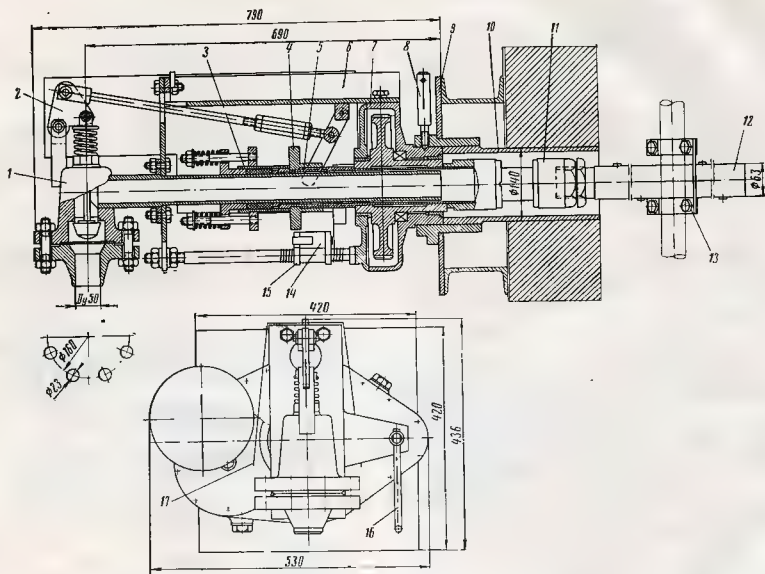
Обдувочный аппарат для конвективных пучков и пароперегревателей типа ОПК-7-58:
